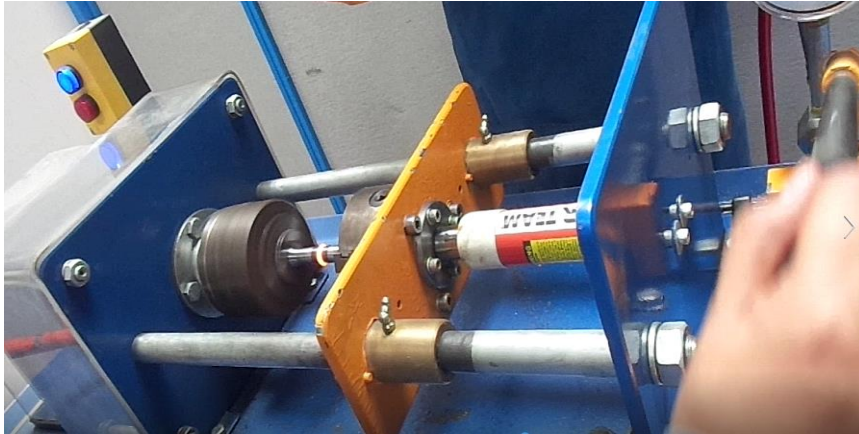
Soldadura por fricción del acero AISI 1045
